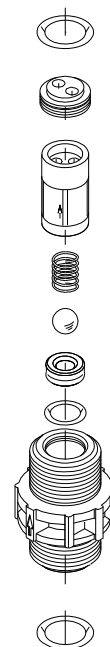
Клапан в исполнении DN 8 (нержавеющая сталь или пластмасса), подпружиненный - по заказу
